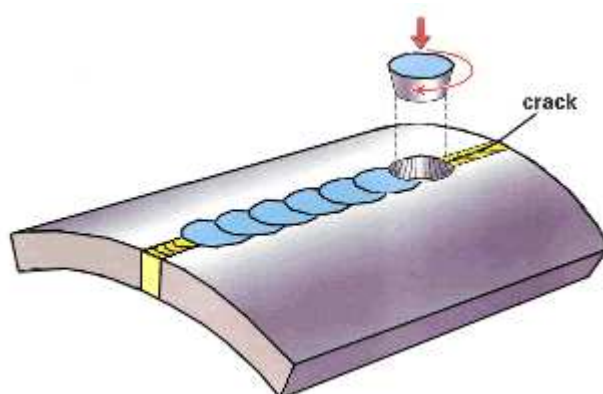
Ilustração do processo de soldagem FTPW (TWI, 2016).
